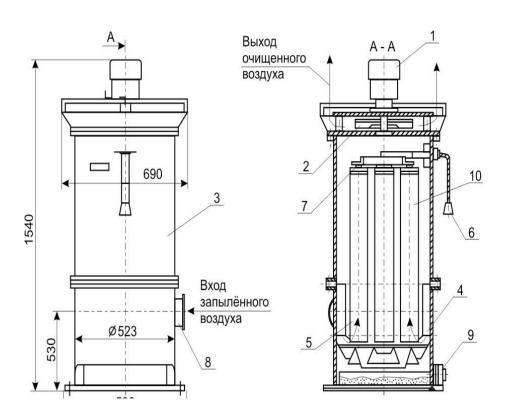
Фильтр рукавный: 1 — двигатель; 2 — вентилятор; 3 — корпус; 4 — фильтр грубой очистки; 5 — фильтр тонкой очистки; 6 — рукоятка встряхивающего механизма; 7 — встряхивающий механизм; 8 — присоединительный патрубок; 9 — бункер с совком; 10 — рукав (www.mnz1.ru)
